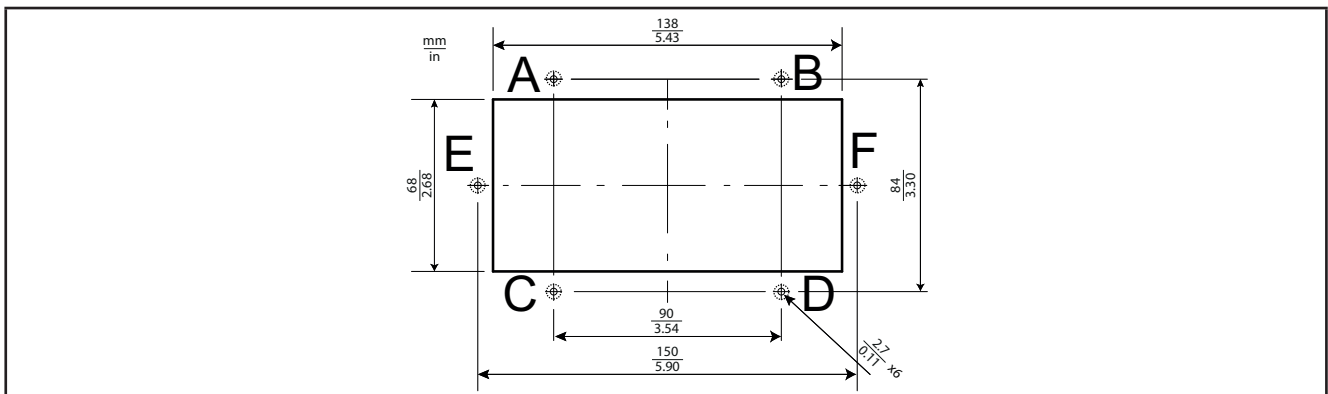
Dimensions ouverture panneau pour EVK PRO DISPLAY
